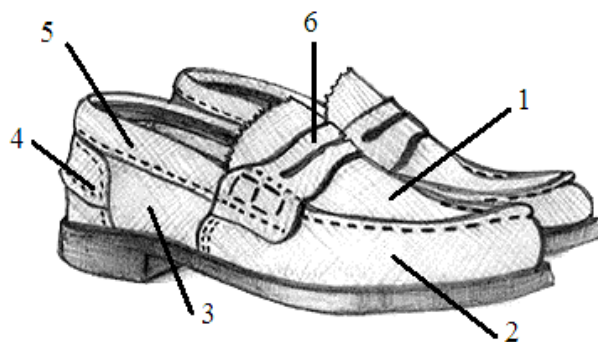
Наружные детали пространственной заготовки полуботинка:
